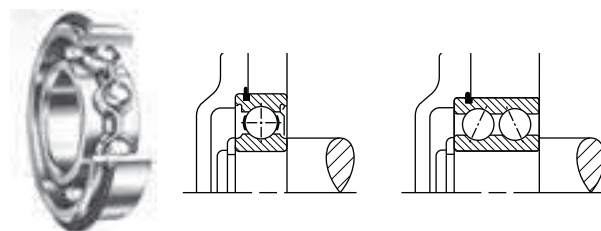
Typische Lagerungen für Lager mit Sprengring
